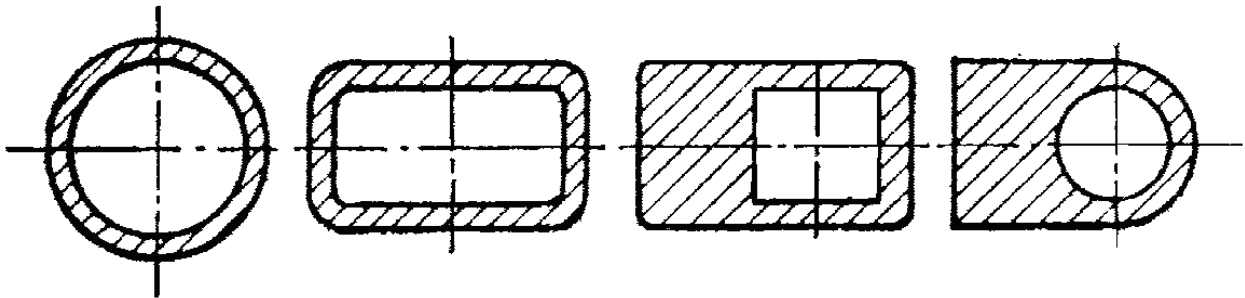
Профили медной трубки, используемой для изготовления индукторов
